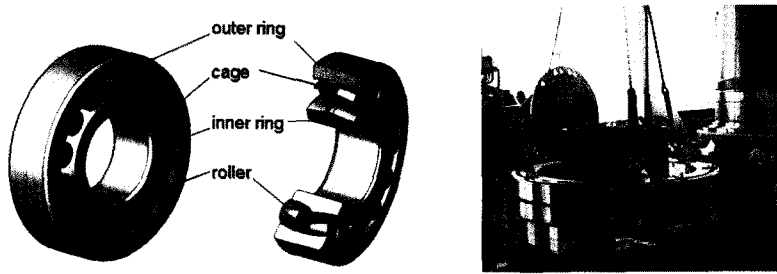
Spherical roller bearing의 구조와 실제 부품의 형상(REpower 5MW형 내부직경 1.5m, 무게 2.7톤)
